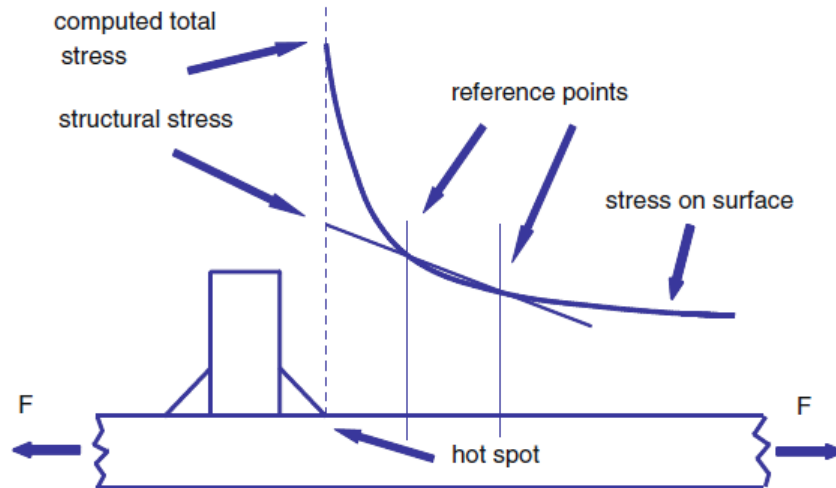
Concentração de tensões no pé de um cordão de soldadura adaptado de Hobbacher, A. (2009)
